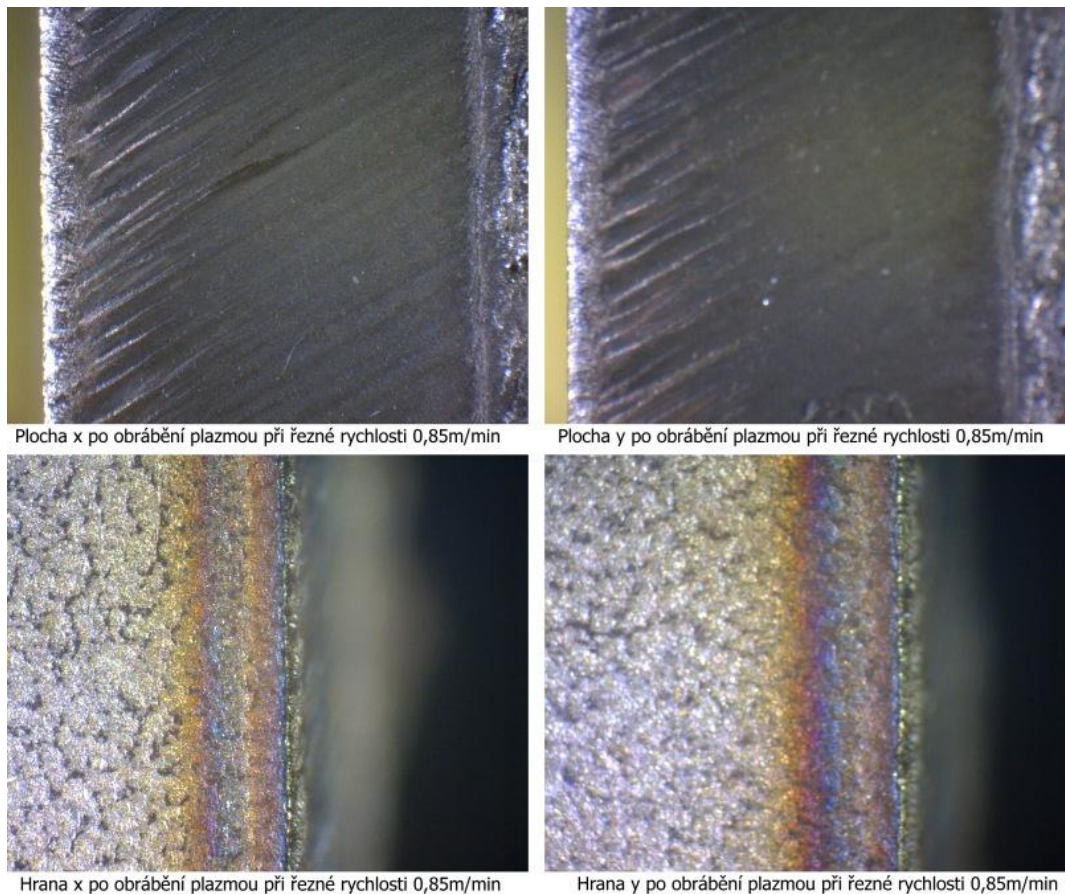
Snímky z mikroskopu vzorku 5 obráběného plazmou - materiál 17 349
